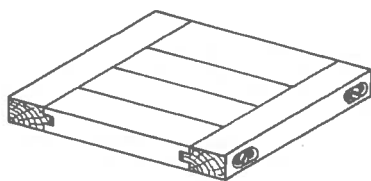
Emboitures embrevées sur le bois de bout d'une planchette en bois massif
